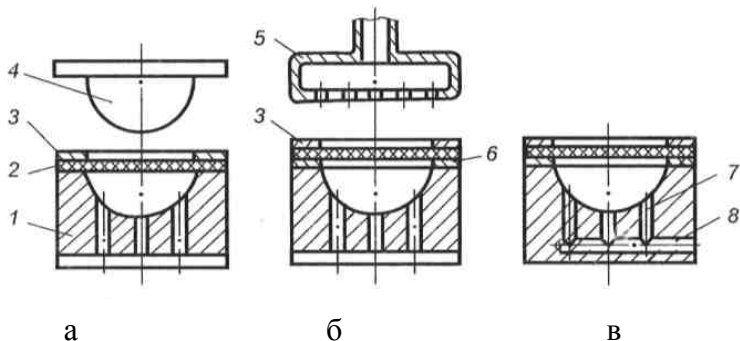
Схеми звичайного (а), пневматичного (б) і вакуумного (в) штампування: 1 – матриця; 2 – заготовка; 3 – притискне кільце; 4 – пуансон; 5 – колектор; 6 – опорне кільце; 7, 8 – канал
